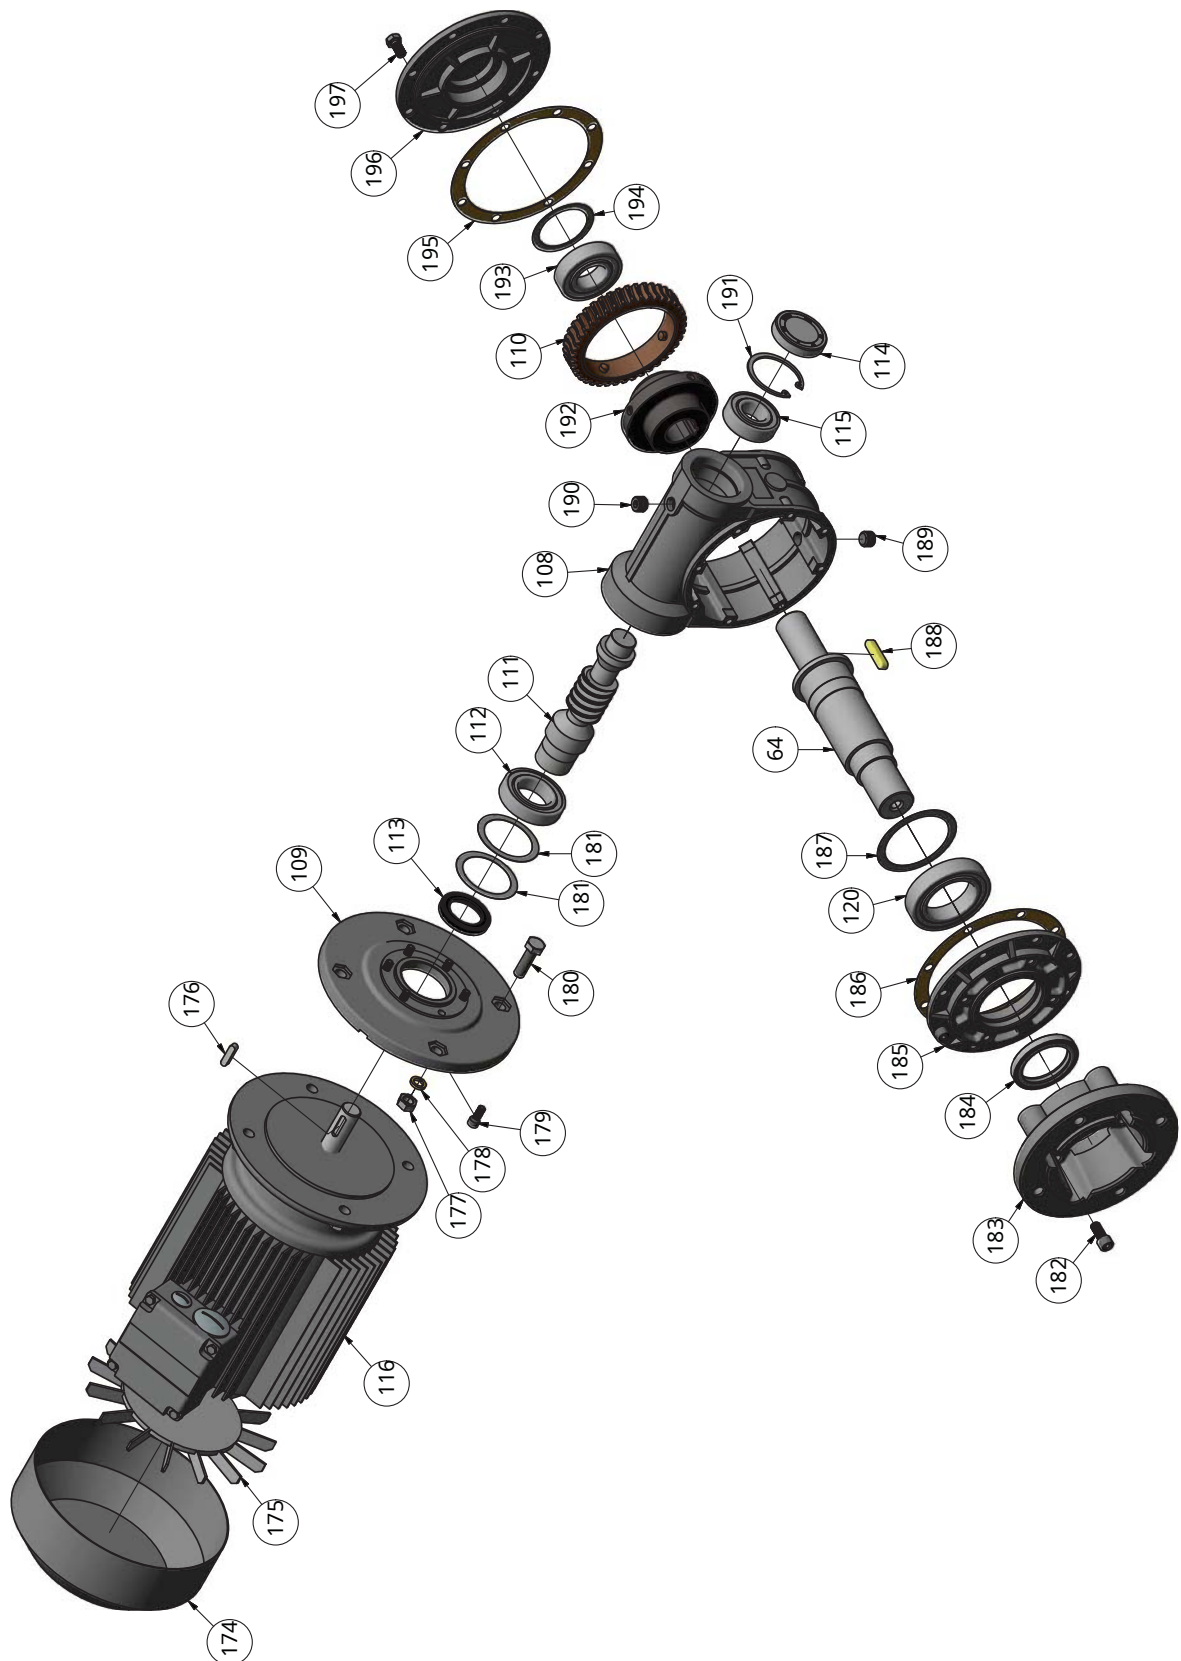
Explosionszeichnung - Dibujo de piezas de repuesto
